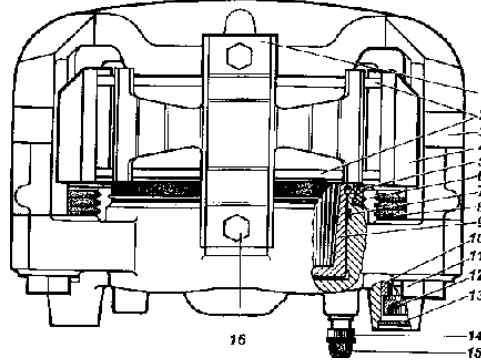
Передние дисковые тормоза: 1 -пружина; 2 -колодки; 3 -скоба; 4 -суппорт, 5 -защитный колпачок; 6 -стопорное кольцо; 7 -уплотнительное кольцо; 8 -защитный чехол; 9 -поршень; 10 -втулка; 11 -болт; 12 -винт; 13 -заглушка; 14 -перепускной клапан; 15 -колпачок; 16 -болты крепления пружины
